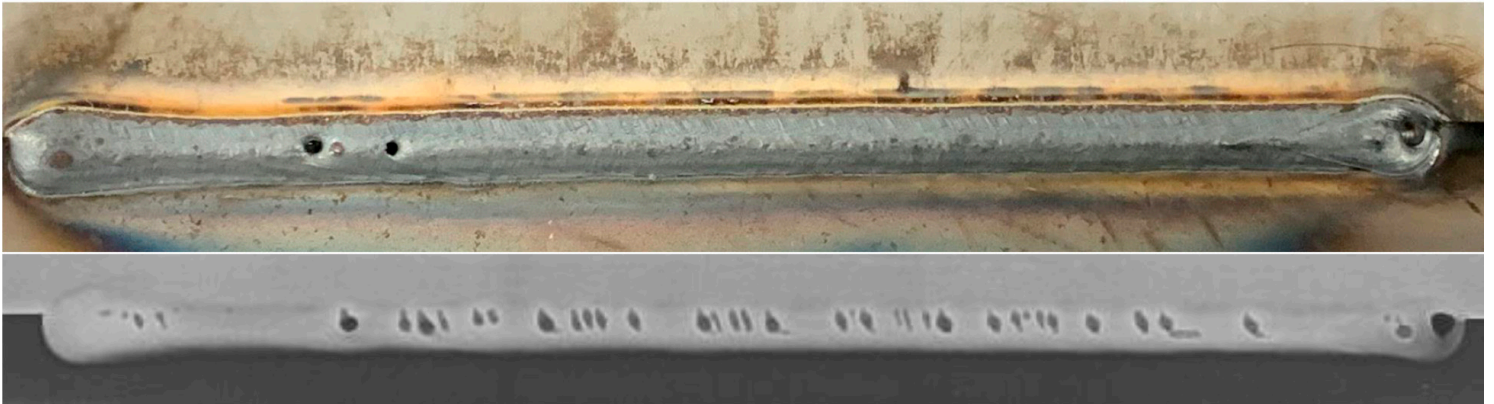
Imagen de la superficie y radiografía digital de las soldaduras que demuestran un 5% o más de porosidad interna. Alambre ER70S-3 soldado en MPH 660GI 60G/60G.
